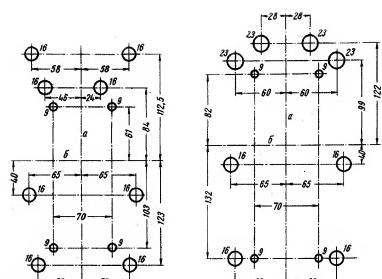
Сверление отверстий для установки на изоляционных пластинах контакторов типа КТП 522 и КТП 542 с задним присоединением
